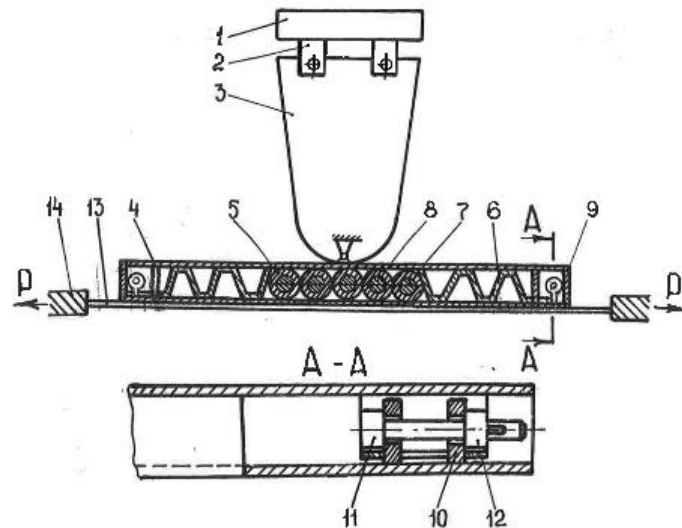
Пуансон для формовки обтяжкой перед изгибом:
